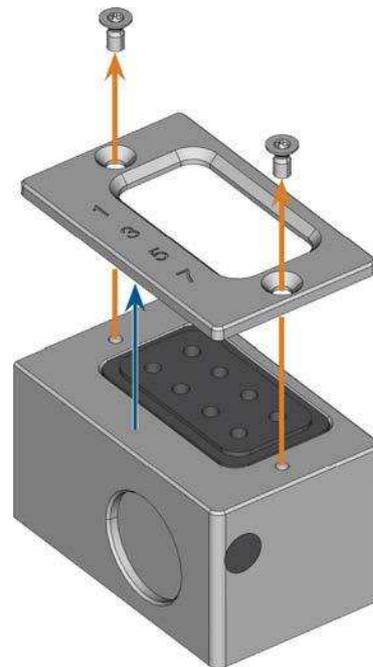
ABDECKUNG DES WERKZEUGMAGAZINS ENTFERNEN
